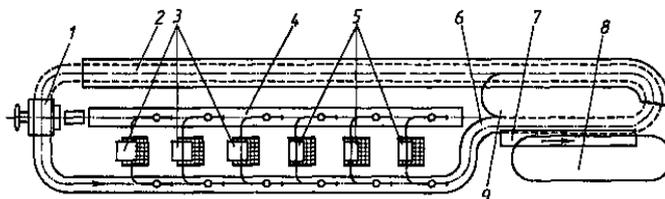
Планировка литейного конвейера для получения средних отливок деталей трактора: 1 – полуавтоматическая выбивная установка; 2 – охлаждающий кожух; 3 – формовочные машины для изготовления нижней полуформы; 4 – пластинчатый конвейер для подачи опок; 5 – формовочные машины для изготовления верхней полуформы; 6 – литейный конвейер; 7 – заливочный транспортер; 8 – подвесной путь для транспортировки жидкого металла; 9 – конвейер для накладывания грузов
